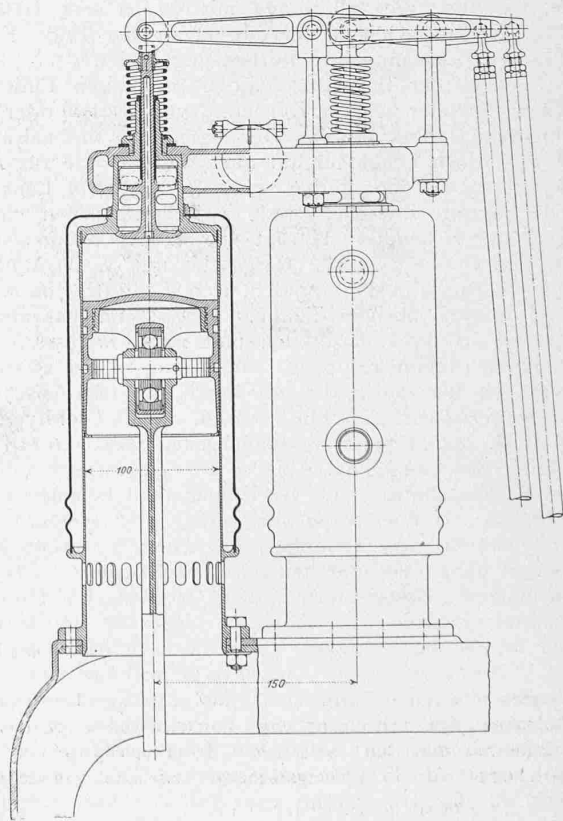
Horizontalschnitt in Zylinderaxe. — Masstab 1:5.
